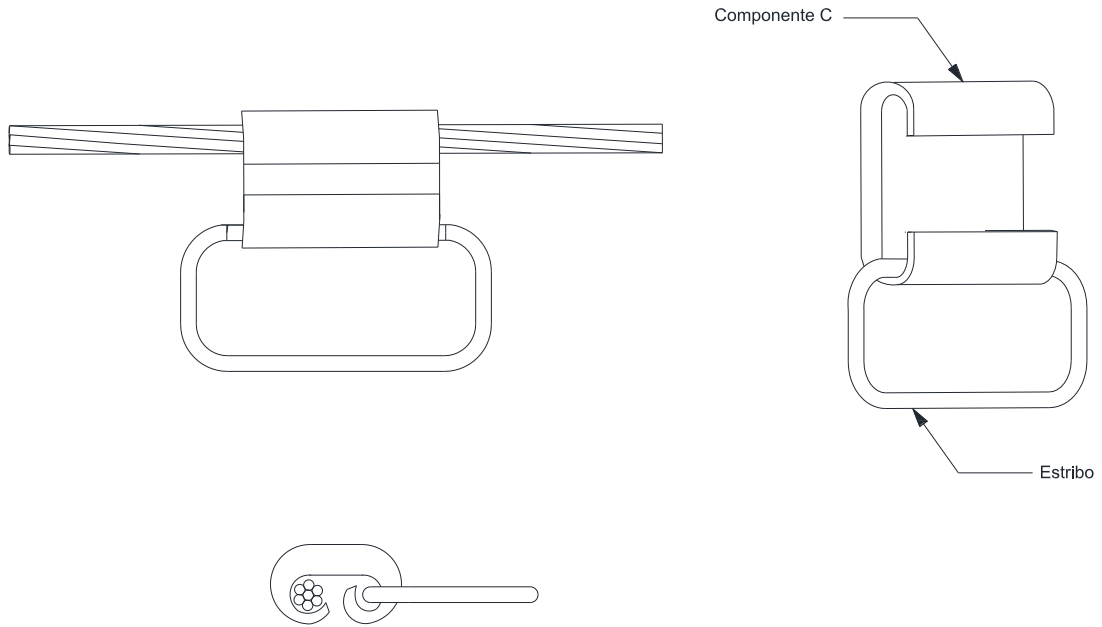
Conexões e emendas – Conector de compressão tipo “C” com estribo
